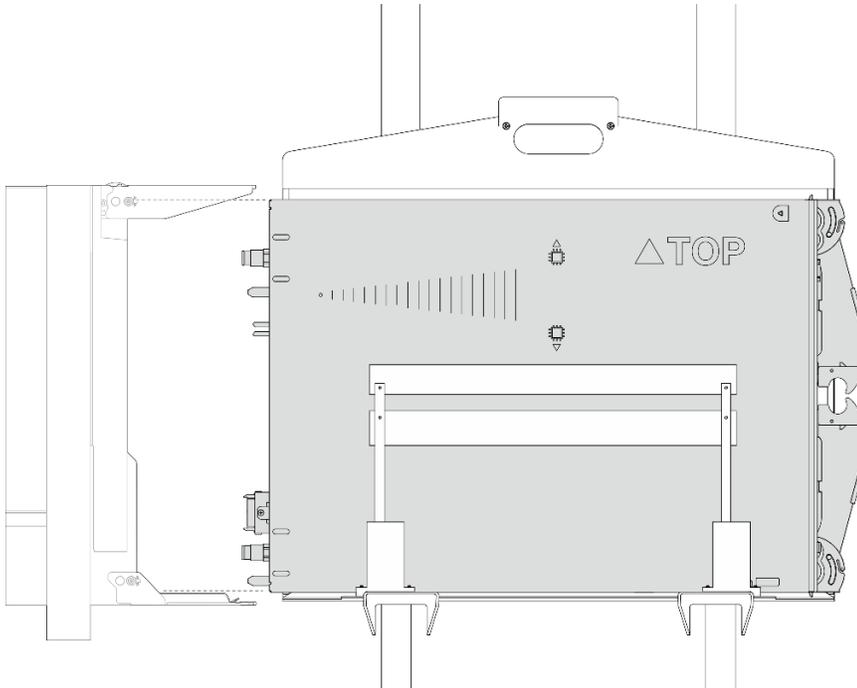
Alignement de la face avant du dispositif sur la face arrière du plateau
